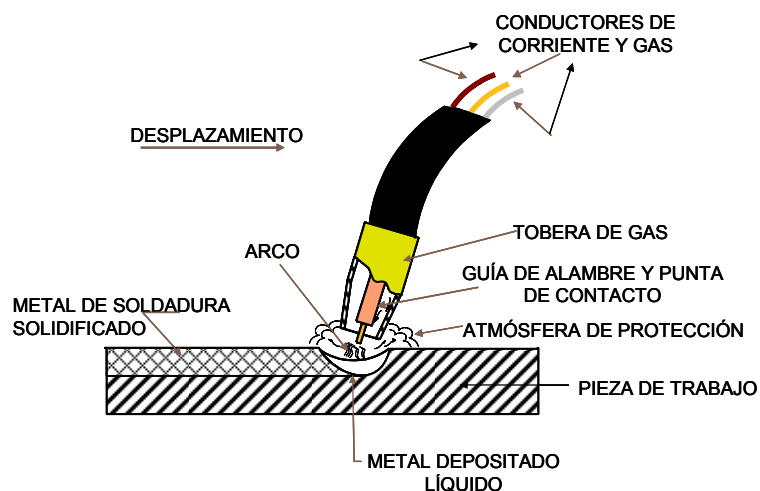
Proceso de soldadura GMAW [7].
